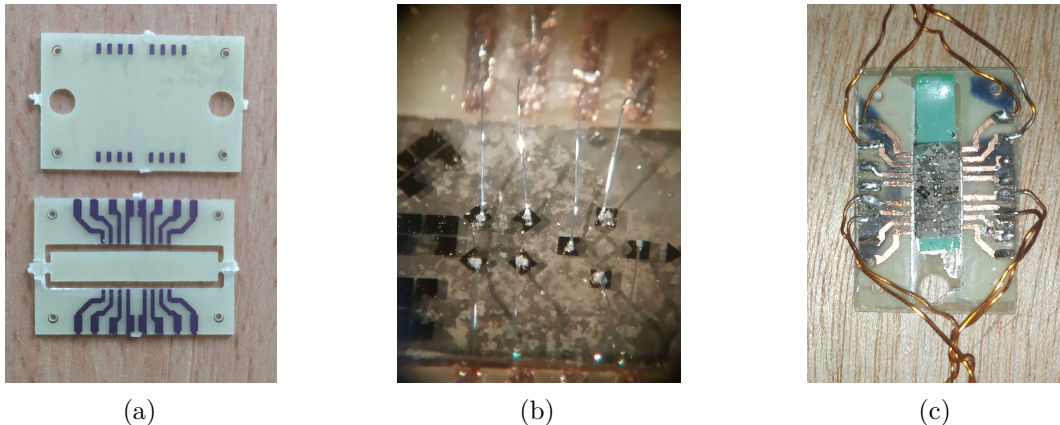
a) PCB et support pour l'échantillon en époxy. b) Connexion métallique aux ponts de Wheatstone via wire bonding. c) Soudure des fils en cuivre pour polariser les dispositifs et réaliser les mesures.
